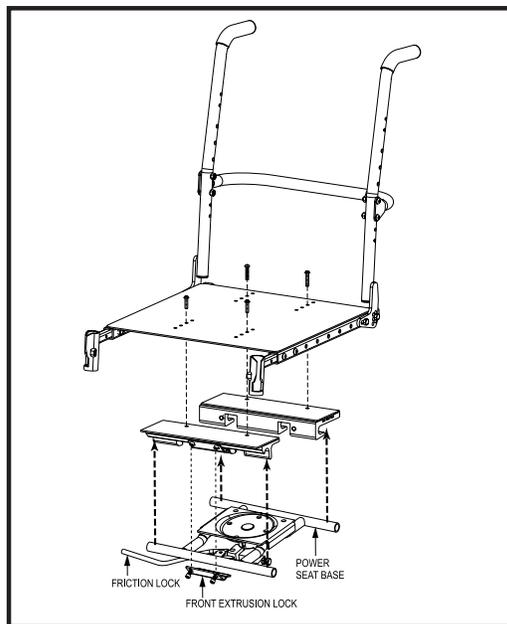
Sistema di montaggio universale (UMS) (Sistema elevazione sedile)
